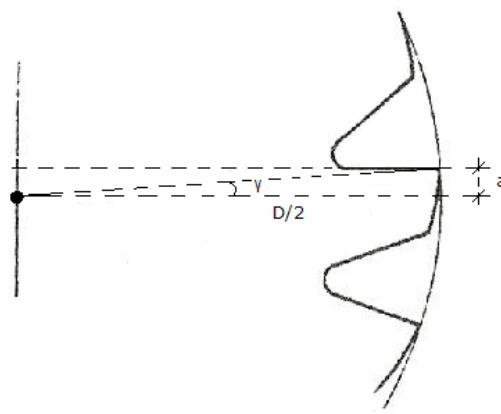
Esquema de la geometría de corte de una fresa madre
